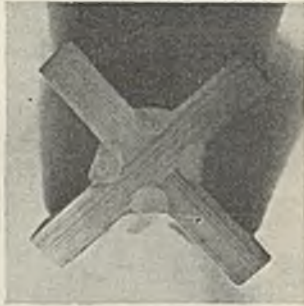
Kreuzprobe, geätzt, Automaten-schweißung.
